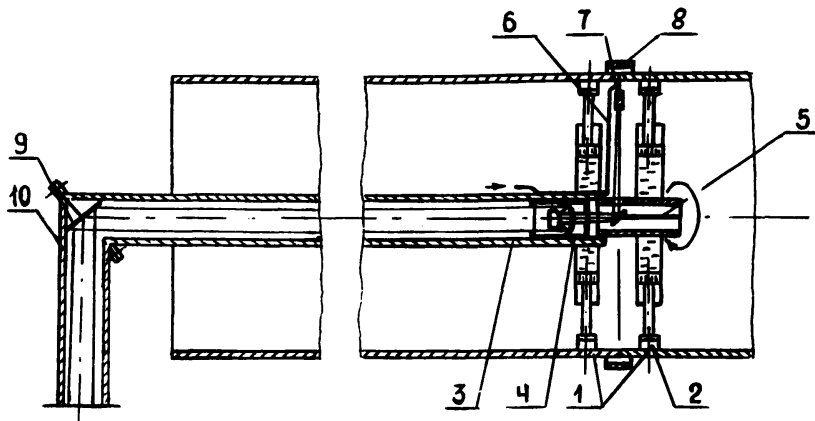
Устройство для сборки и сварки неповоротного стыка лазерным лучом.
